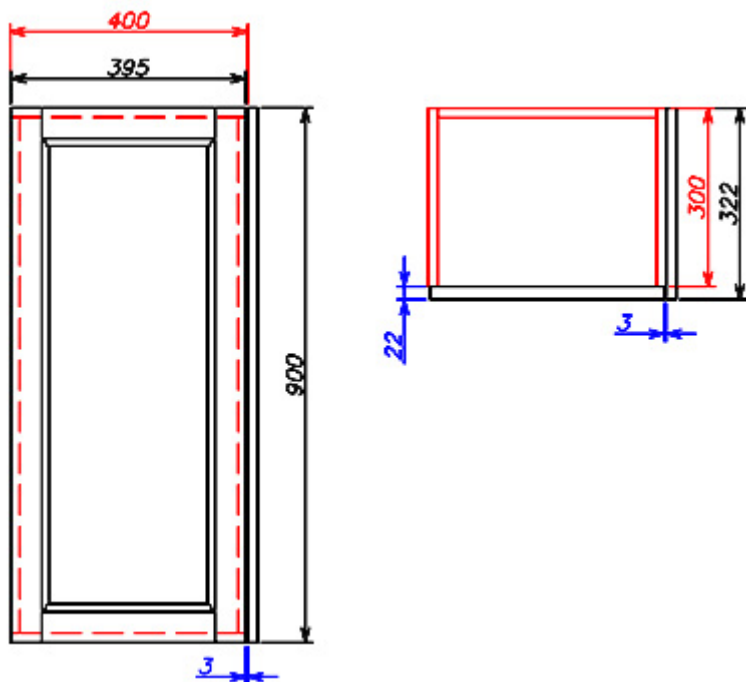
Накладка на боковину корпуса (вид спереди и сверху)
